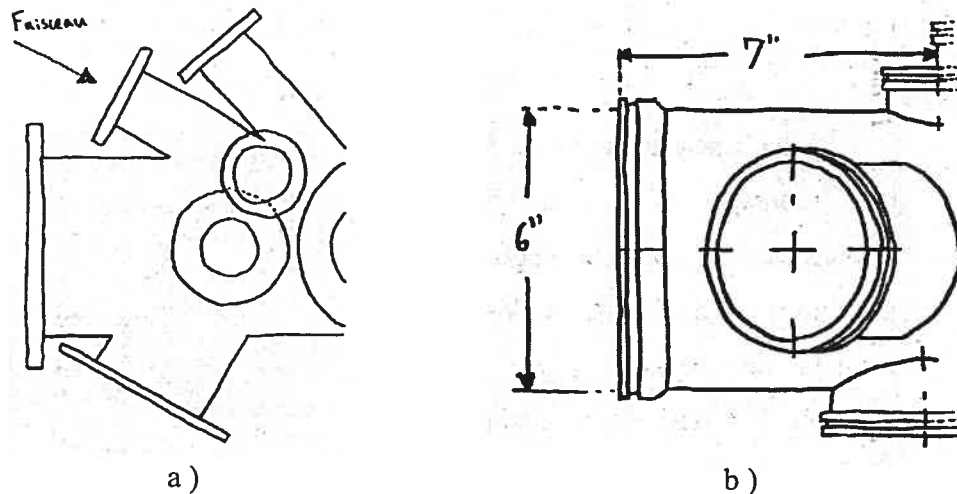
a) chambre vue de dessus, b) chambre vue de côté
